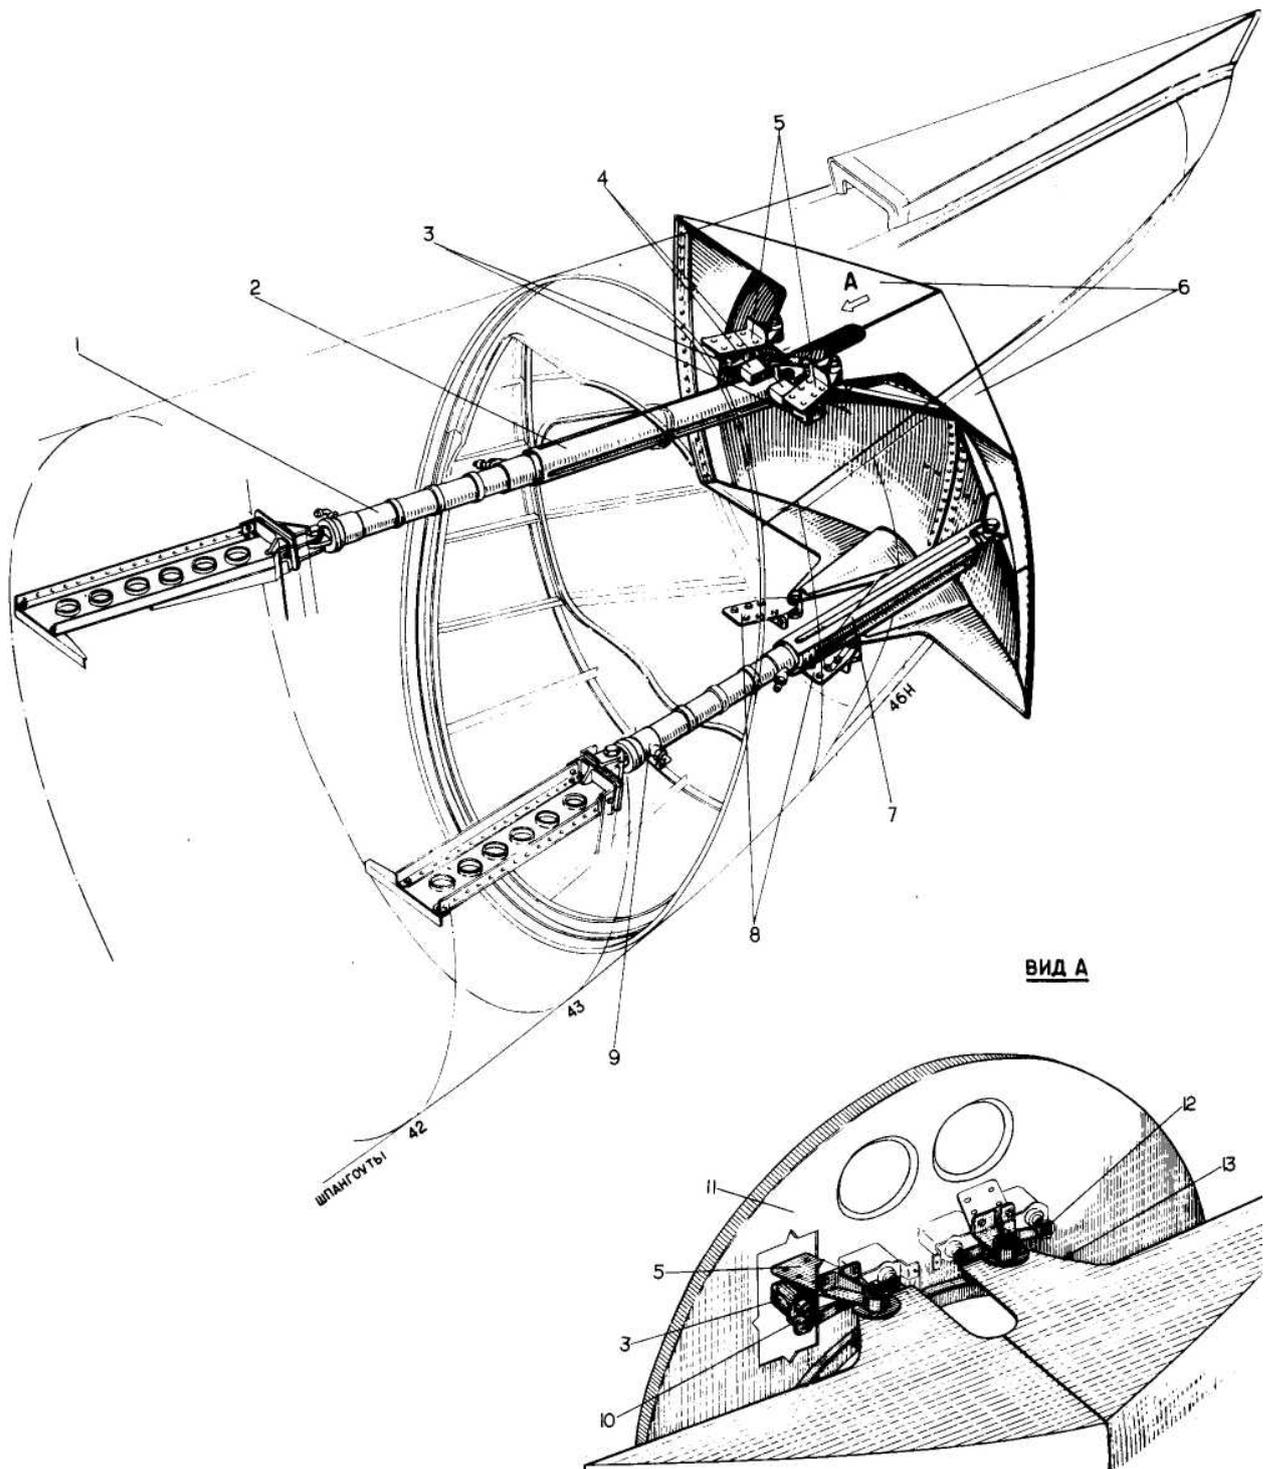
УСТАНОВКА РЕВЕРСИВНО-ТОРМОЗНЫХ ШИТКОВ
